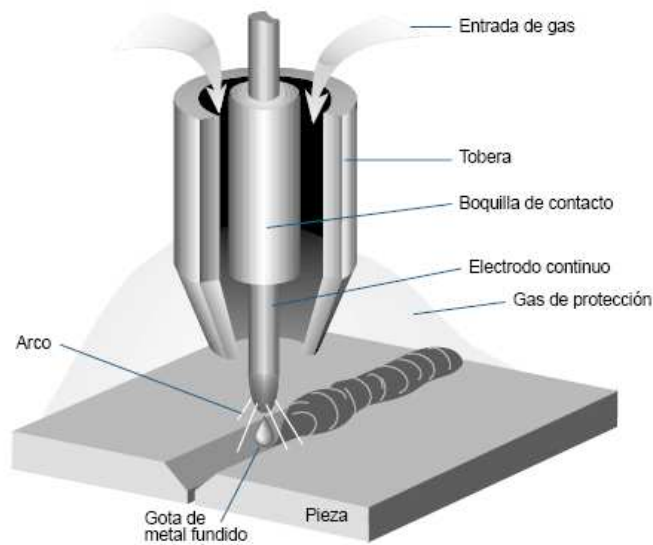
Esquema del proceso de soldadura GMAW
